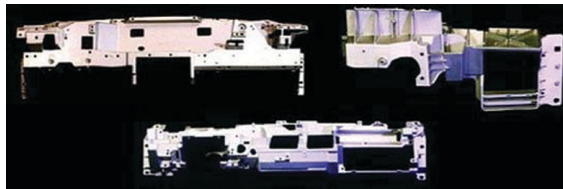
Instrument panel, 기존에는 32piece의 제품을 용접하여 적용하였으나 마그네슘으로는 1 piece로도 가능함.
